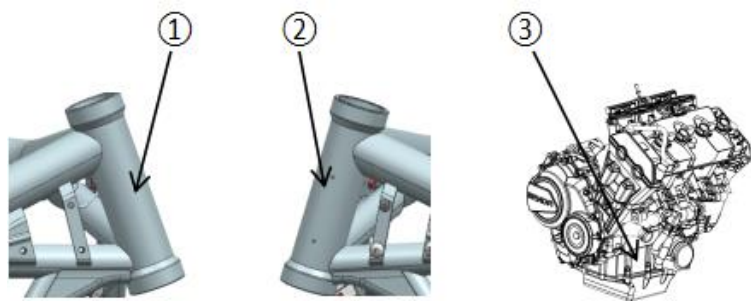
Расположение заводской таблички, номера рамы мотоцикла (VIN) и номера двигателя
